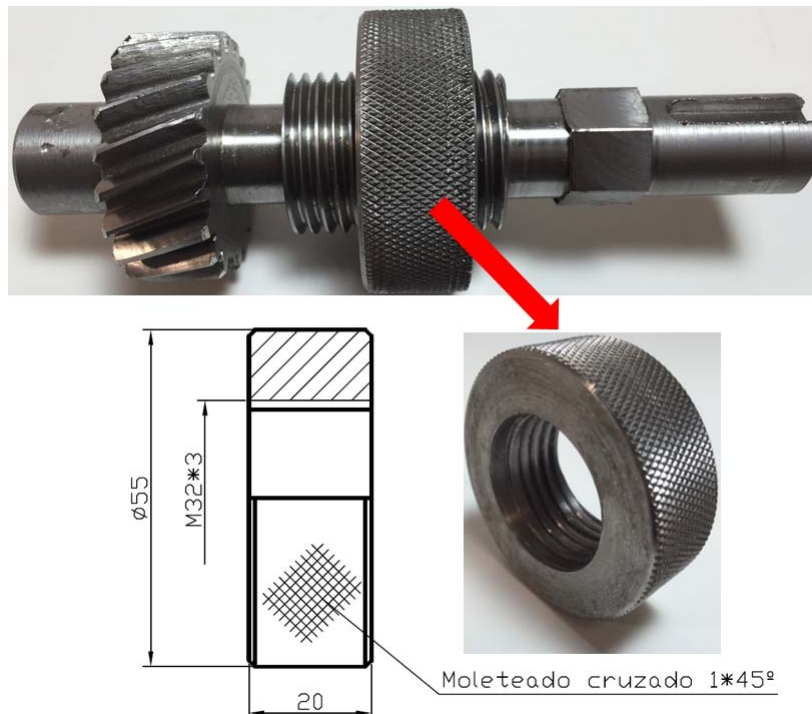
Tuerca a mecanizar. Roscado interior y moletado.
